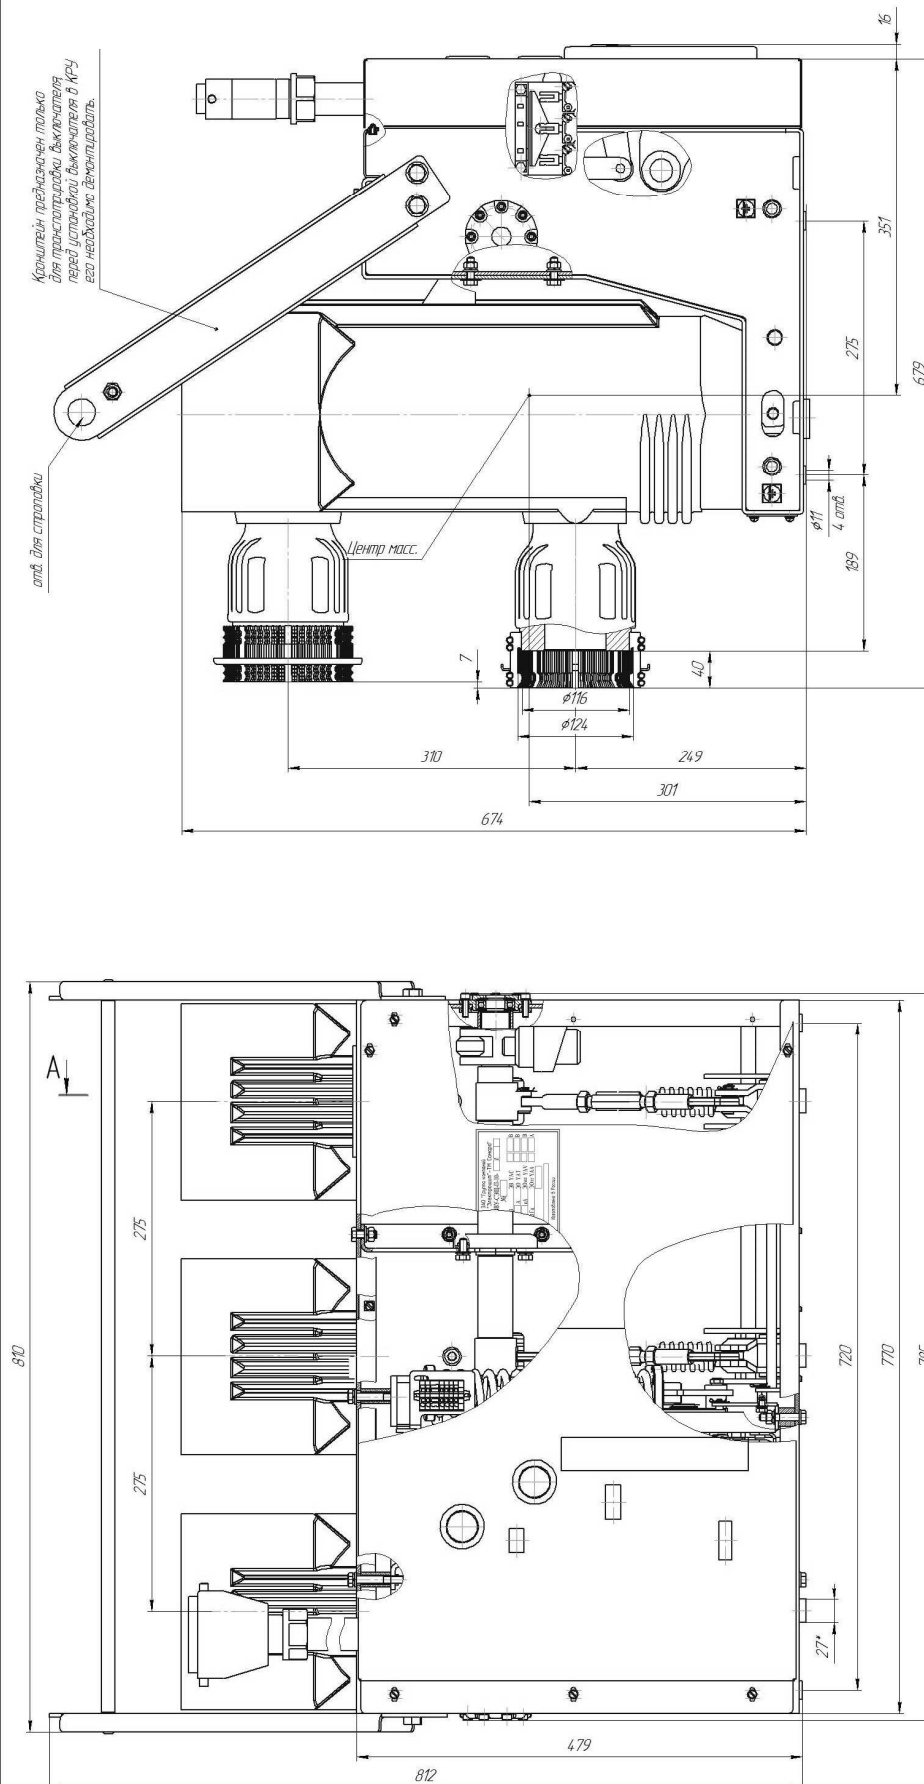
Габаритные, присоединительные и установочные размеры выключателя типа ВВУ-СЭЦ-П-10-20(31,5)/η (СЭЦ-70)
